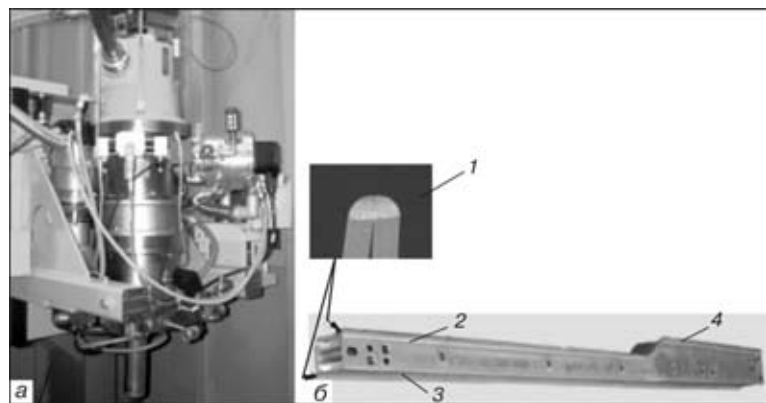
Электронно-лучевая пушка для безвакуумной сварки (а) и пример использования ее для сварки полых элементов из алюминия (б): 1 — поперечное сечение и расположение сварного соединения на полых элементе из алюминия; 2, 3 — шов; 4 — изделие
